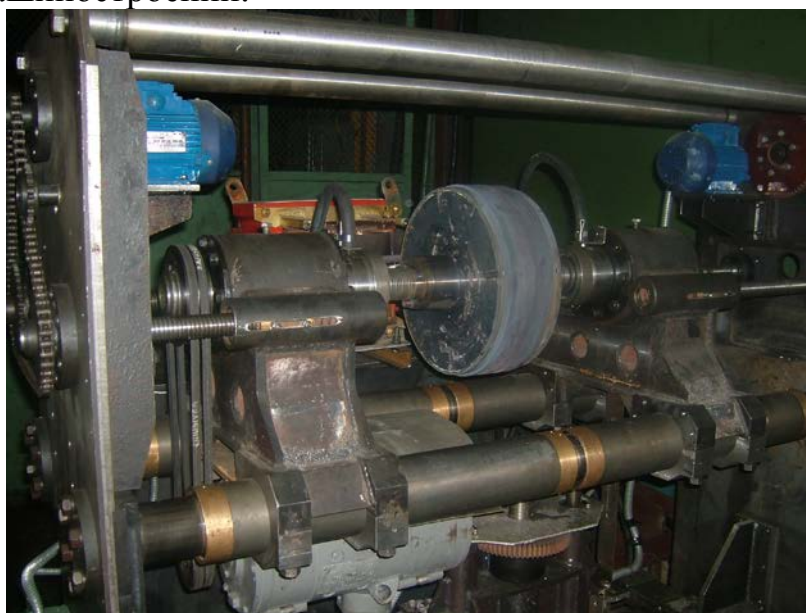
Модернизированная установка центробежной индукционной наплавки покрытий
